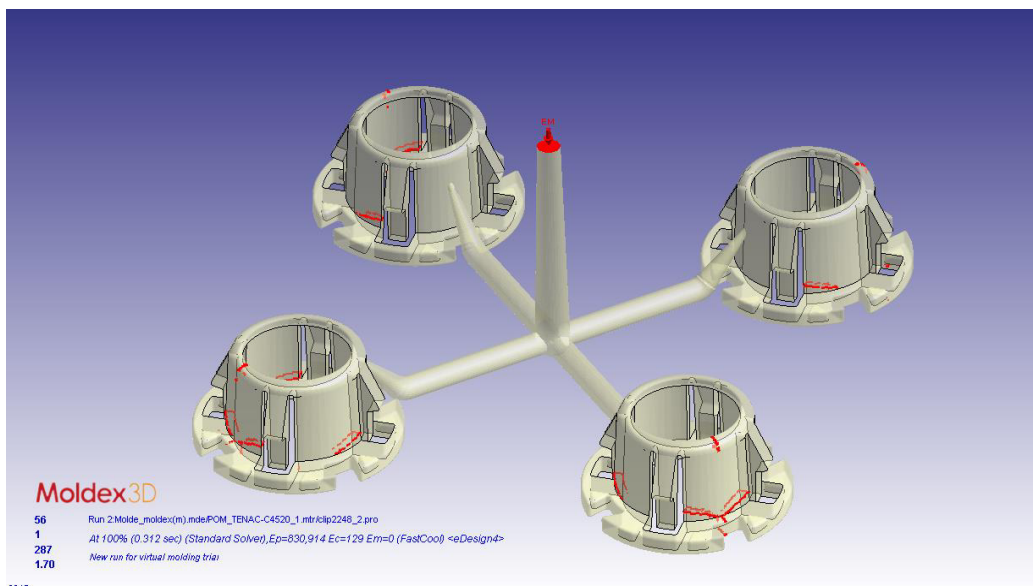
Localização das linhas de soldadura das moldações do Projeto A
